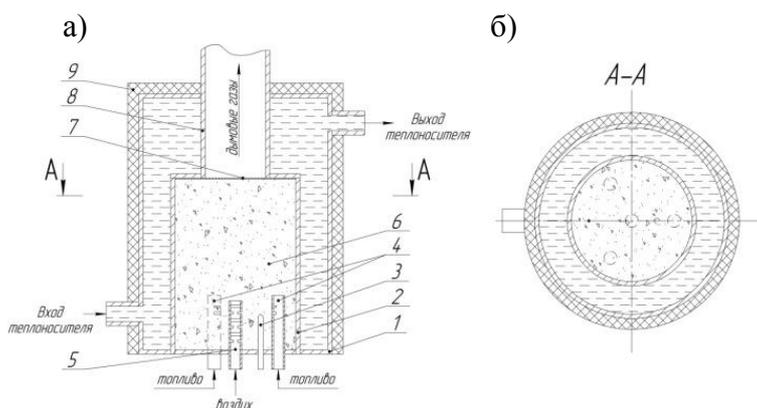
Продольный (а) и поперечный (б) разрезы теплогенерирующей установки на жидких углеводородных отходах: 1 – корпус; 2 – камера сгорания; 3 – запальный элемент; 4 – топливные инжекторы; 5 – воздушный инжектор; 6 – пористый наполнитель (криптол); 7 – стальная сетчатая насадка; 8 – канал продуктов сгорания; 9 – тепловая изоляция
